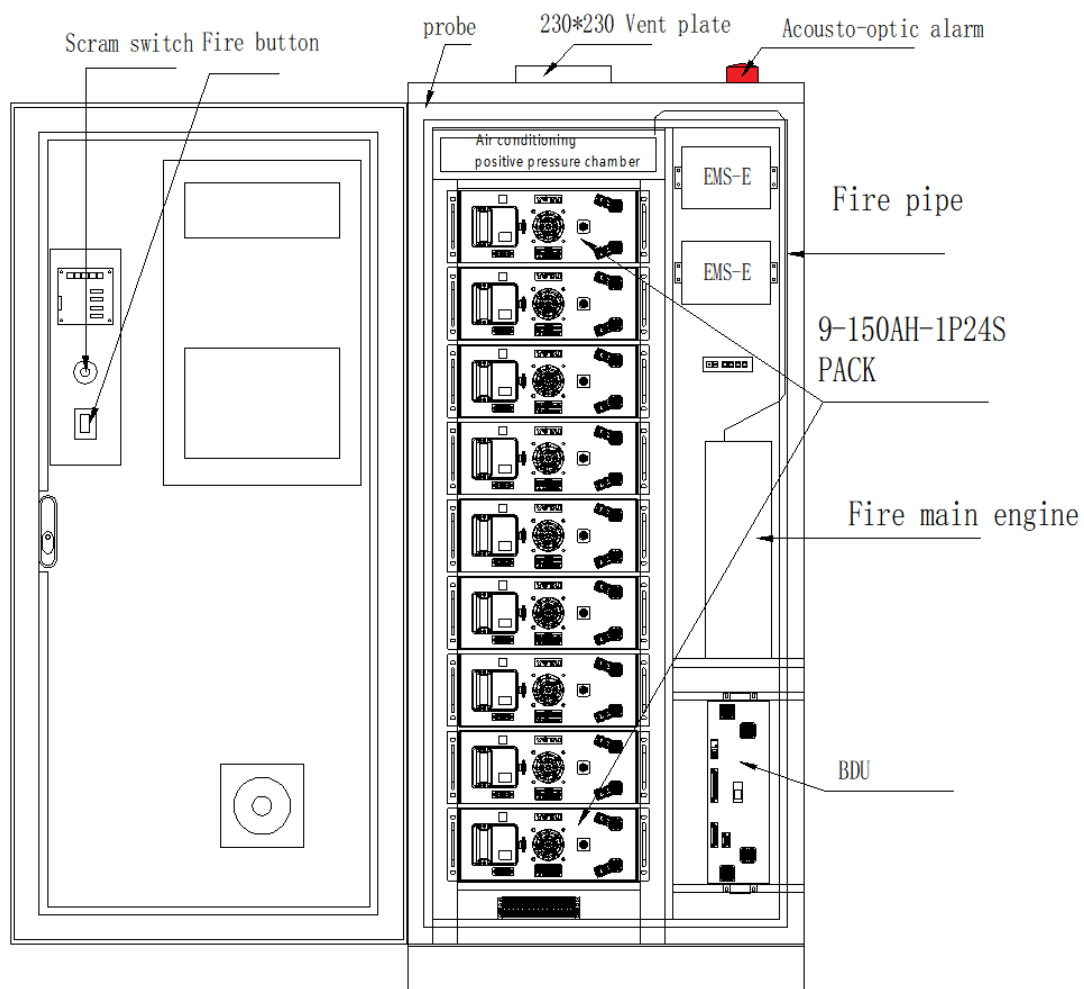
Grundrissdiagramm des Feuerlöschsystems
